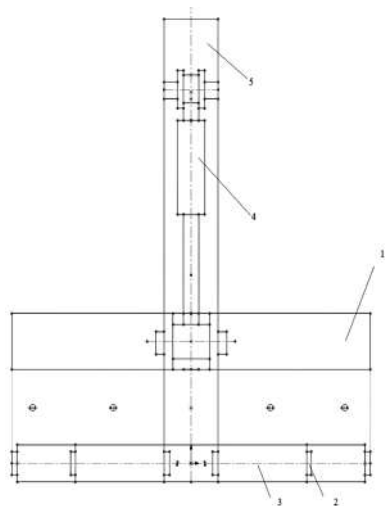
Ковш для очистки и уплотнения сечения каналов: 1-корпус ковша; 2-съемная опора; 3-уплотняющий ролик; 4-гидроцилиндр; 5-рукоять экскаватора.
